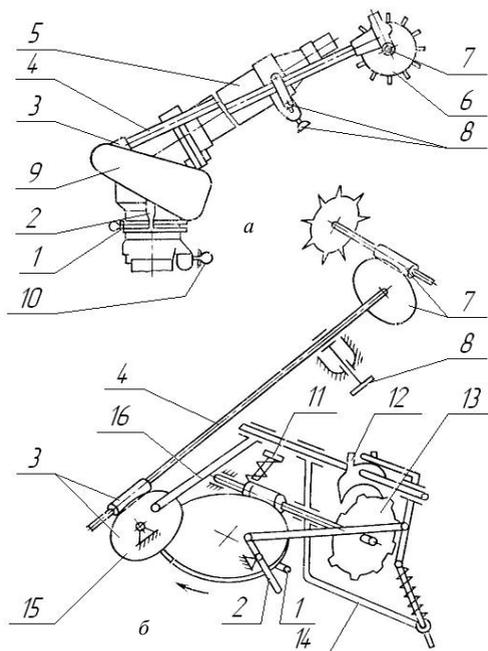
Дальнеструйный аппарат типа ДД: *а* – общий вид; *б* – кинематическая схема механизма поворота ствола; 1 – упор; 2 – толкатель реверса; 3 – нижний редуктор; 4 – вал; 5 – ствол; 6 – турбинка; 7 – верхний редуктор; 8 – фиксирующий и регулирующий винты; 9 – механизм поворота; 10 – упор; 11 – тормоз; 12 – собачка; 13 – храповое колесо; 14 – коромысло; 15 – ходовой редуктор; 16 – шатун
